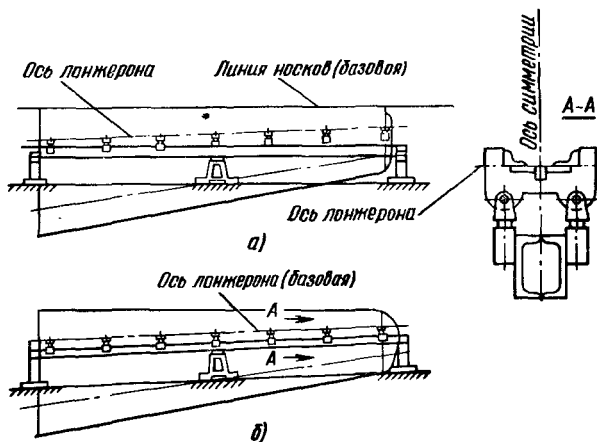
Определение базовых осей приспособления для сборки носка крыла:
